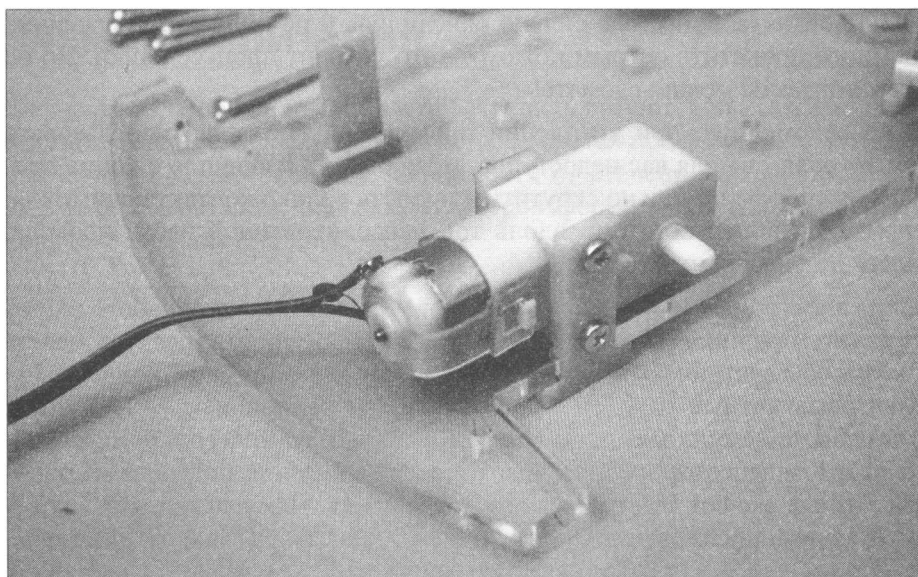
Установка двигателя на Т-образные крепления в корпус робота
